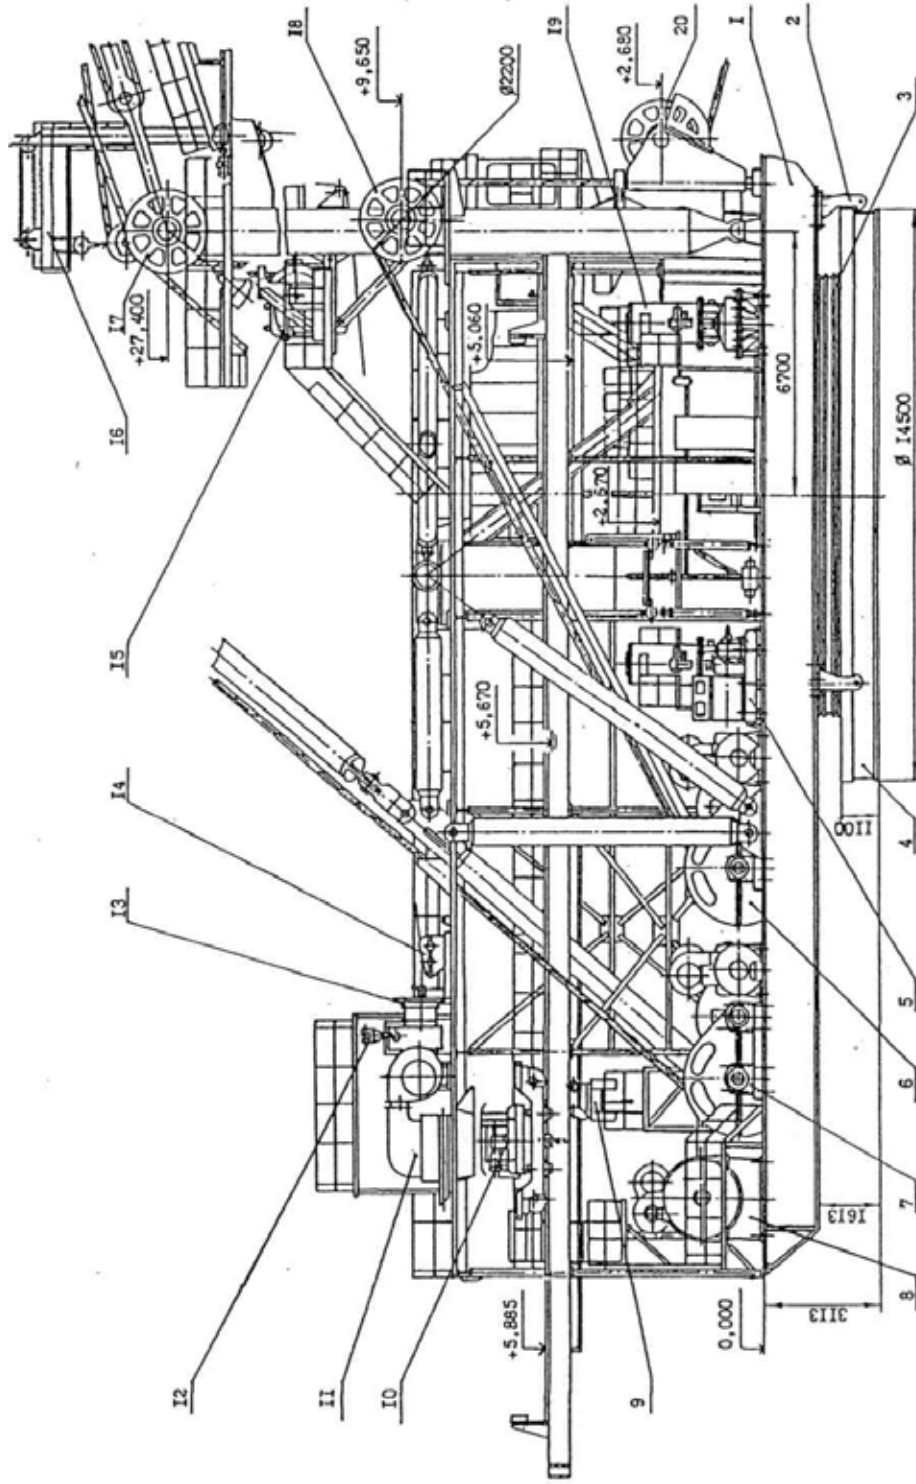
Механизмы и оборудование на платформе экскаватора ЭШ20/90 (продольный разрез) 1.Платформа поворотная; 2.Захват опорной рамы; 3.Устройство опорно-поворотное; 4.Рама опорная; 5.Установка насоса НР-1250/32; 6.Лебедка тяговая; 7.Лебедка подъемная; 8.Агрегат преобразовательный; 9.Тельфер г/п 3,2 тс; 10.Кран мостовой г/п 20 тс; 11.Система вентиляции; 12.Тельфер г/п 1 тс; 13.Система охлаждения
